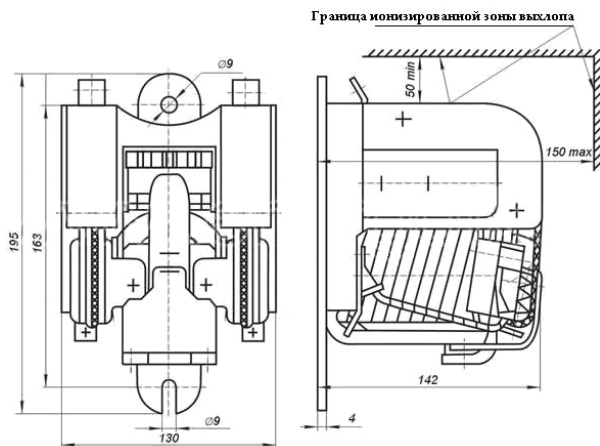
Габаритные, установочные размеры КПД-121 У2
